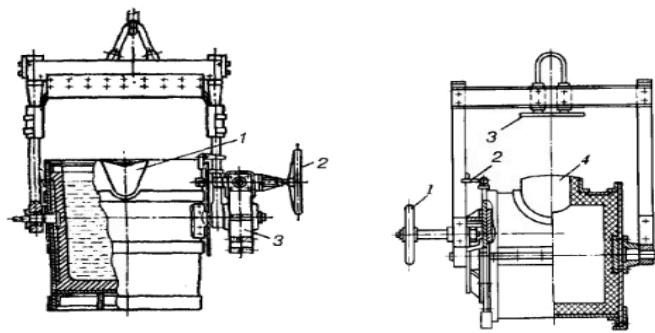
Поворотные чайниковый (а) и барабанный (б) разливочные ковши. а: 1 - носок; 2 - штурвал; 3 - червячный механизм; б: 1 - штурвал; 2 - предохранительная скоба; 3 - экранирующий щиток; 4 - сливной носок
